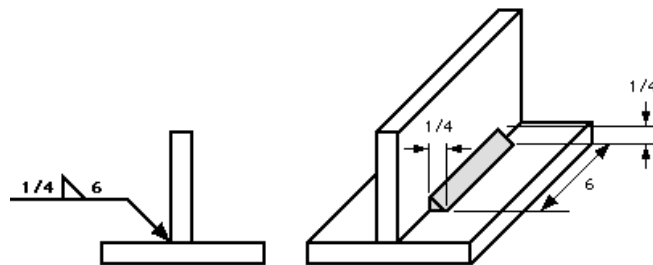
Soldadura de filete (Longitud del Cordón)
